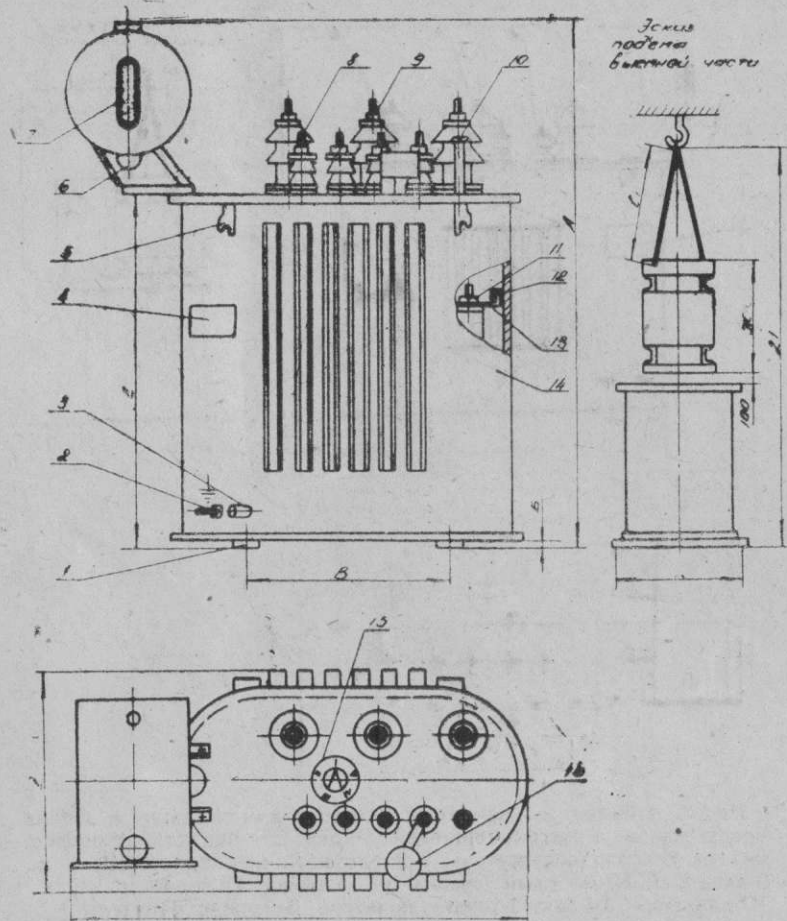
1-пластина (швеллер); 2-заземление; 3-пробка для заливки и отбора пробы масла; 4-щиток мощности; 5-крюк для подъема трансформатора; 6-воздухоосушитель; 7-маслоуказатель; 8-ввод НН; 9-ввод ВН; 10-ртутный термометр; 11-гайка; 12-скоба; 13-пластина; 14-бак; 15-переключатель; 16-предохранитель (устанавливается по требованию заказчика).
